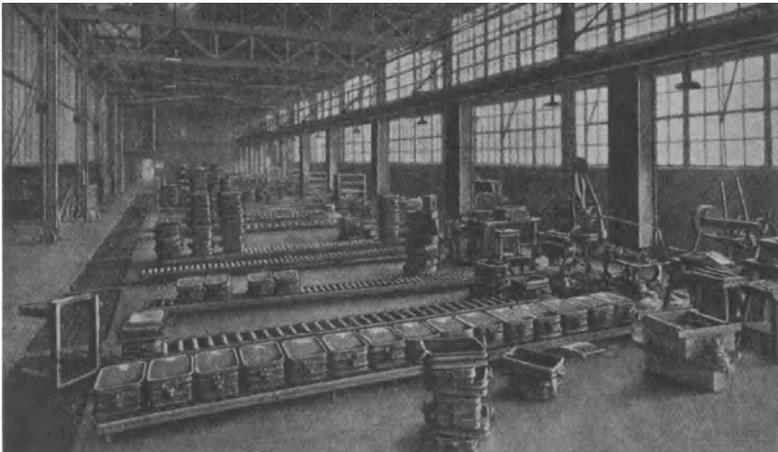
Formmaschinen mit Rollenförderern (Cadillac).
